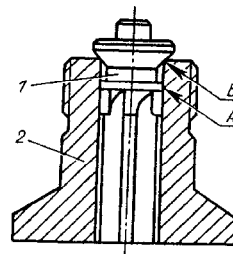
Клапан 4 нагнетательный /рис. 55/
